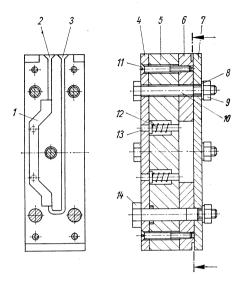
Werkzeug mit technischen Hilfsmitteln zur Entformung;
